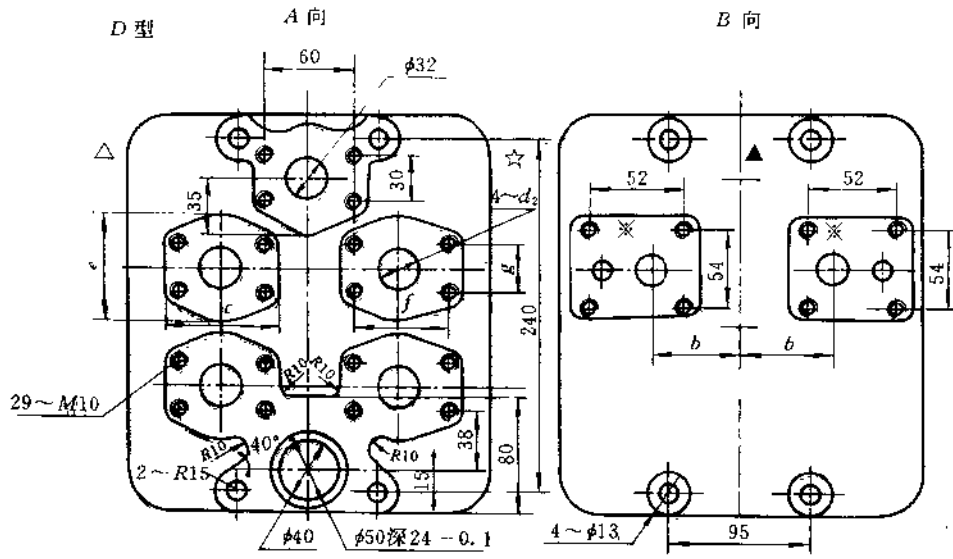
DF 型二联多路阀 D 型外形尺寸
